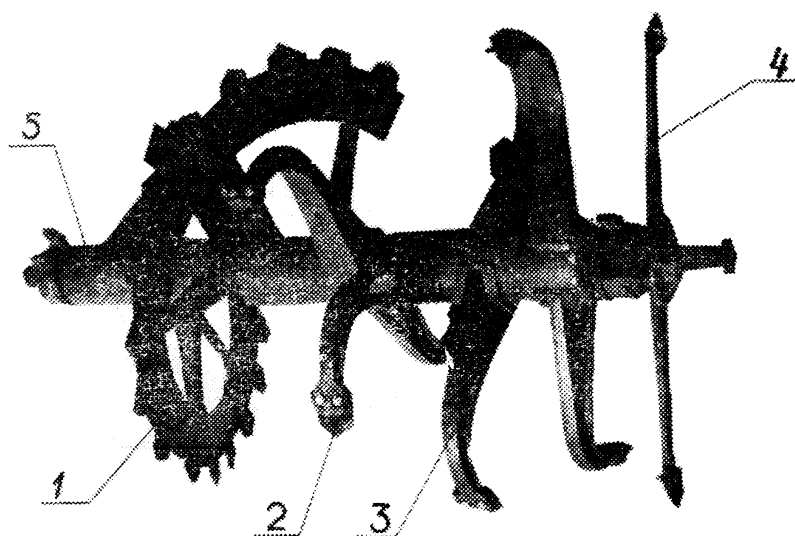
Фреза навантажувача: 1 – шнекова частина; 2 – ріжучі ножі; 3 – лапи з ножами; 4 – відсікач матеріалу, який не навантажується; 5 – вал
